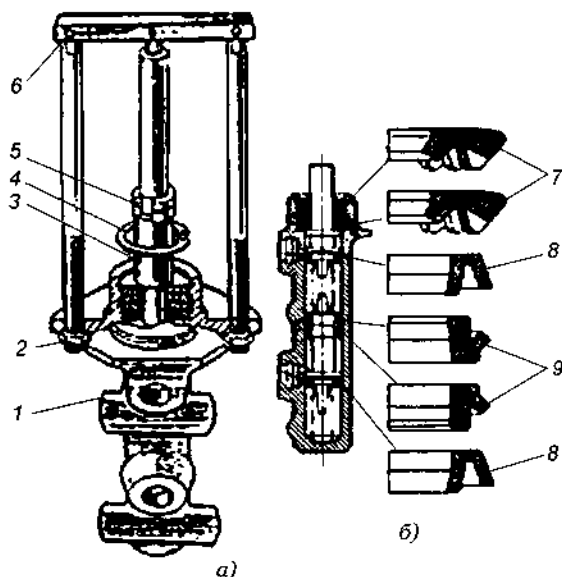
Приспособление для сборки главного тормозного цилиндра: *а* — установка главного тормозного цилиндра; *б* — расположение манжет; 1 — цилиндр; 2 — стойка; 3 — шток; 4 — запорное кольцо; 5 — полукошце; 6 — траверса; 7, 8, 9 — манжеты
